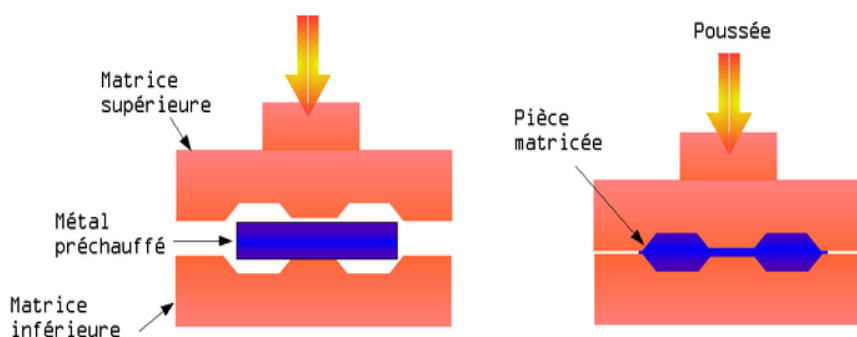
Schéma d'élaboration par forgeage (pièces forgées).
